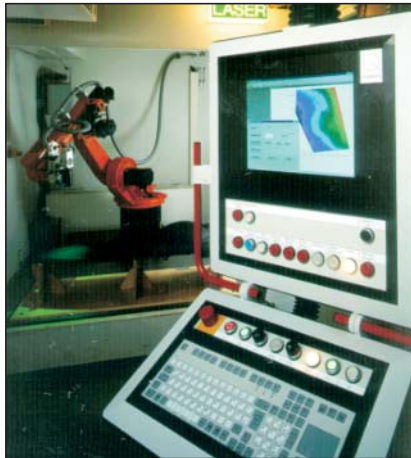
Mobile Prüfanlage für hinter-schäumte Bauteile
